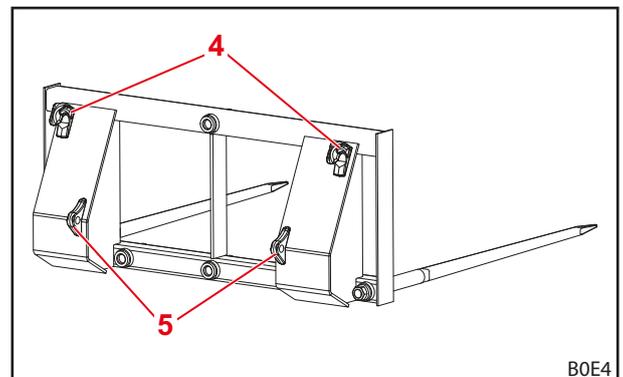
Estructura del pincho para pacas H – Vista posterior
